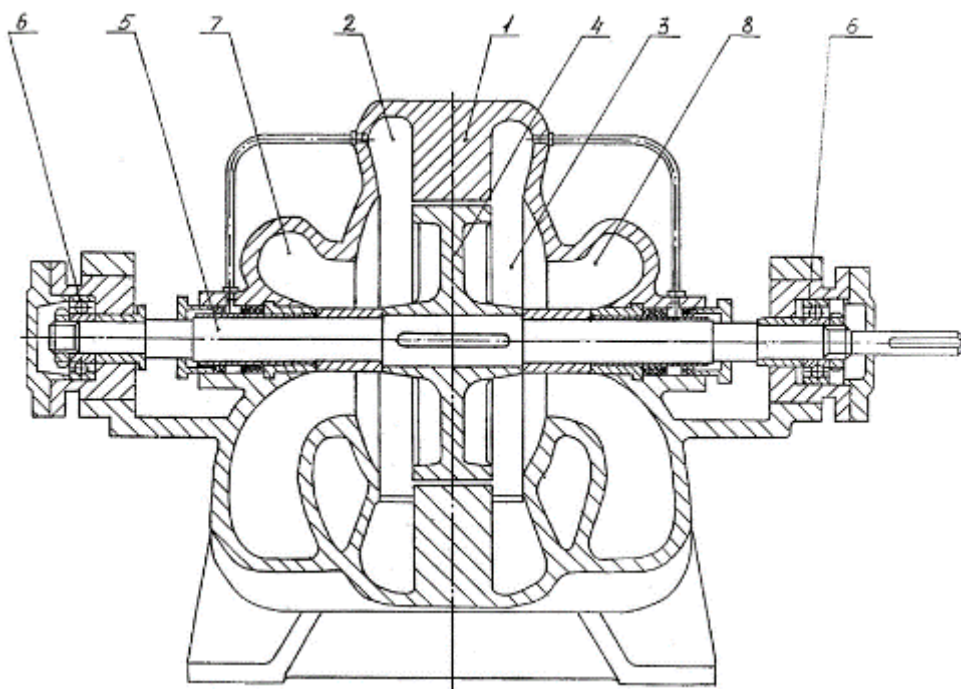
Насос за пат. № 37350: 1 – корпус; 2, 3 – вихрова камера; 4 – робоче колесо; 5 – вал; 6 – підшипникова опора; 7, 8 – напівспіральний канал
